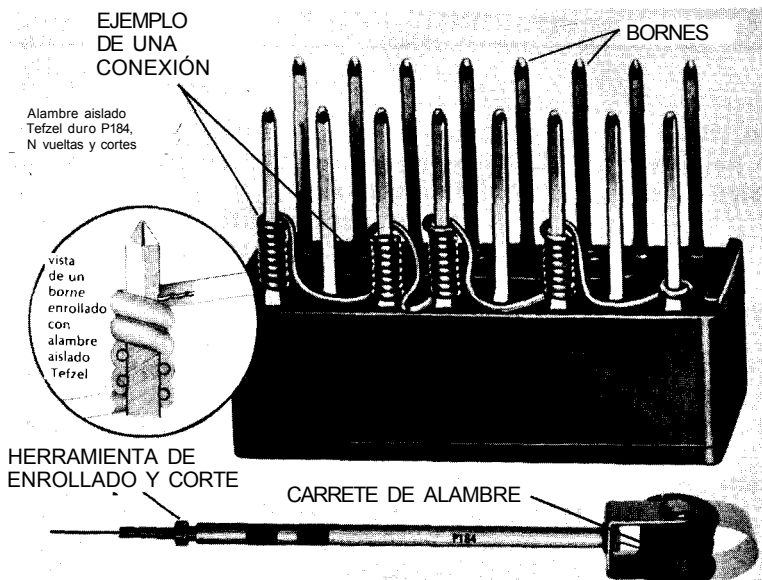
Conexión enrollada que emplea una herramienta de acción rápida (OK Machine and Tool Corporation).
